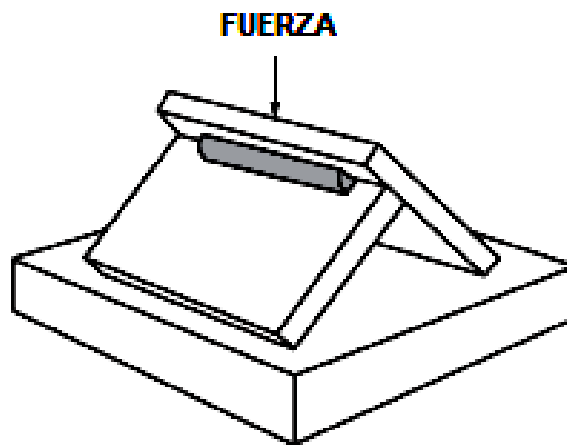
MÉTODO DE ROTURA DE ENSAYO PARA CALIFICACIÓN DE SOLDADORES PUNTEADORES (1)
